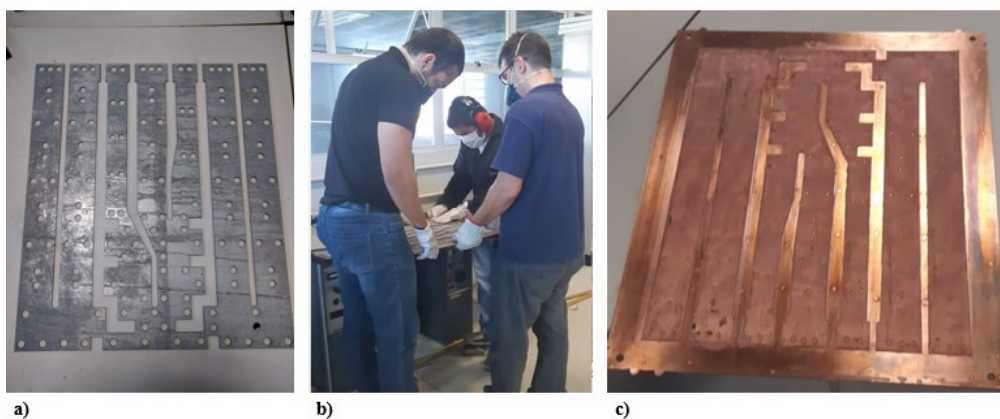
a) Gabarito de solda para fixação da malha. b) Realização da solda-ponto para fixação da malha. c) Chapa de fechamento do evaporador com as camadas de malha fixadas.
